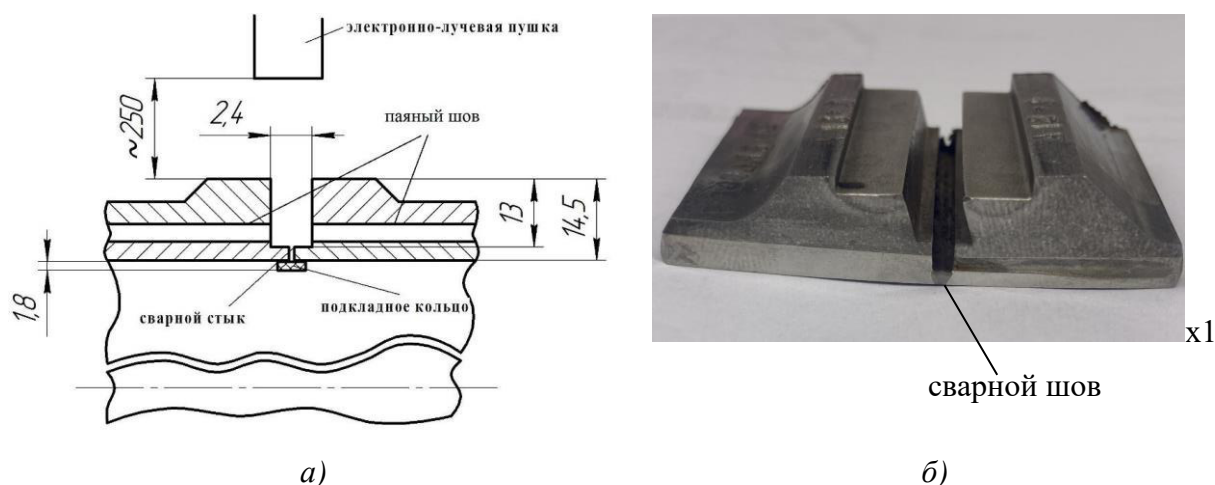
Эскиз сварного соединения (а) и внешний вид сваренного образца с натурного узла (б)
